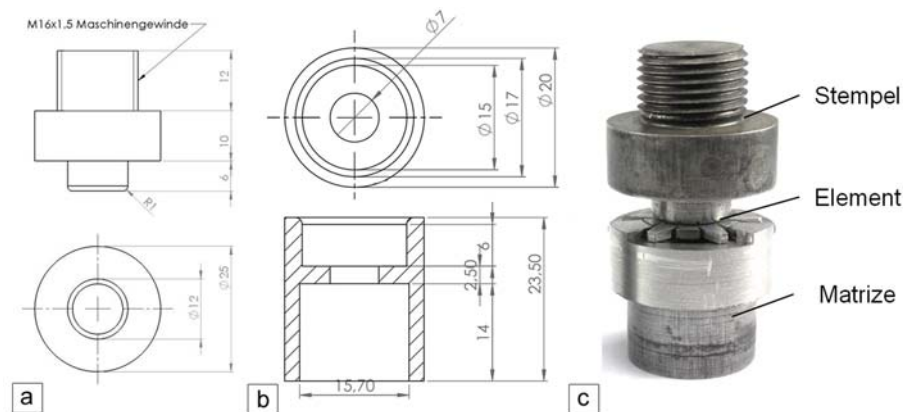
Zeichnung von Stempel (a) und Matrize (b); Werkzeug mit einem Element (c)
